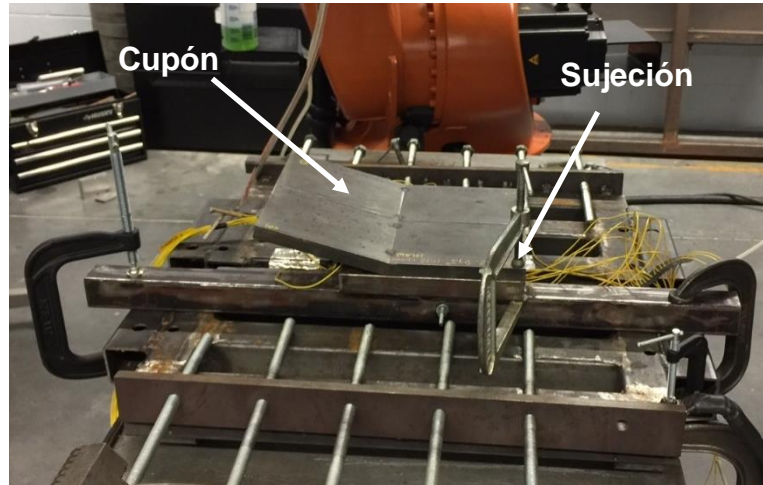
14. Sistema de sujeción del cupón soldado.
